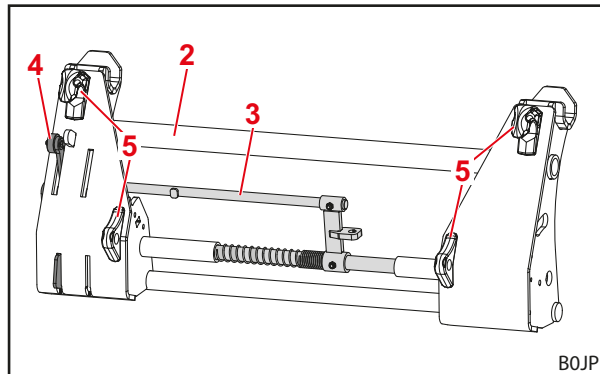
Structure de l'adaptateur d'outil MX – Vue arrière
